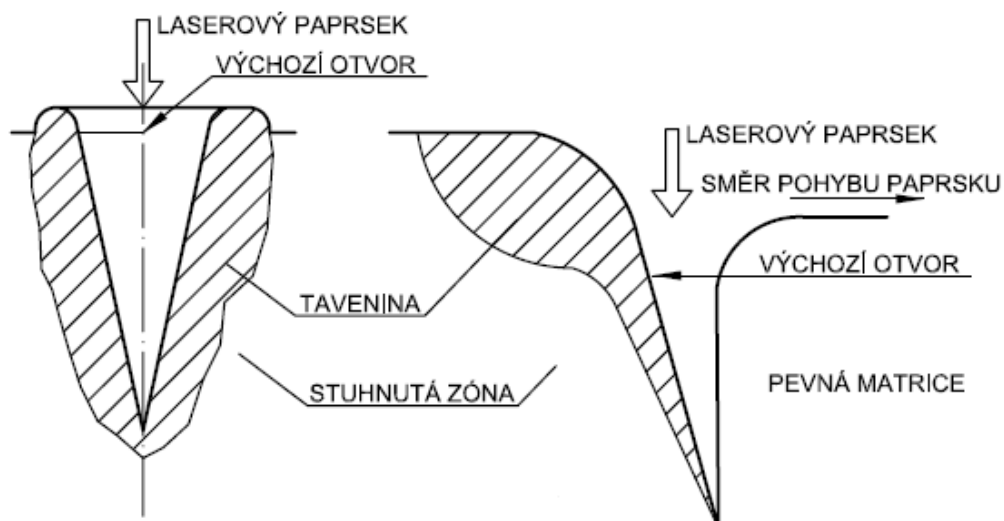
Účinek laserového paprsku při dopadu na obráběný materiál [7]
